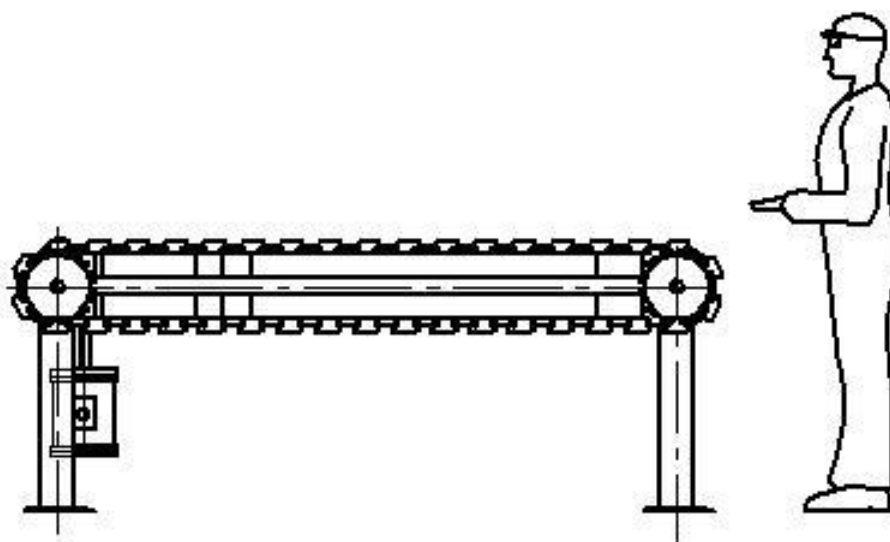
Загрузка деталей на транспортёр-накопитель
